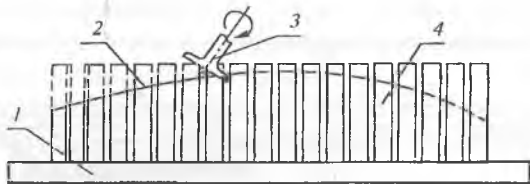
Обработка контура сотового блока на фрезерном станке:
